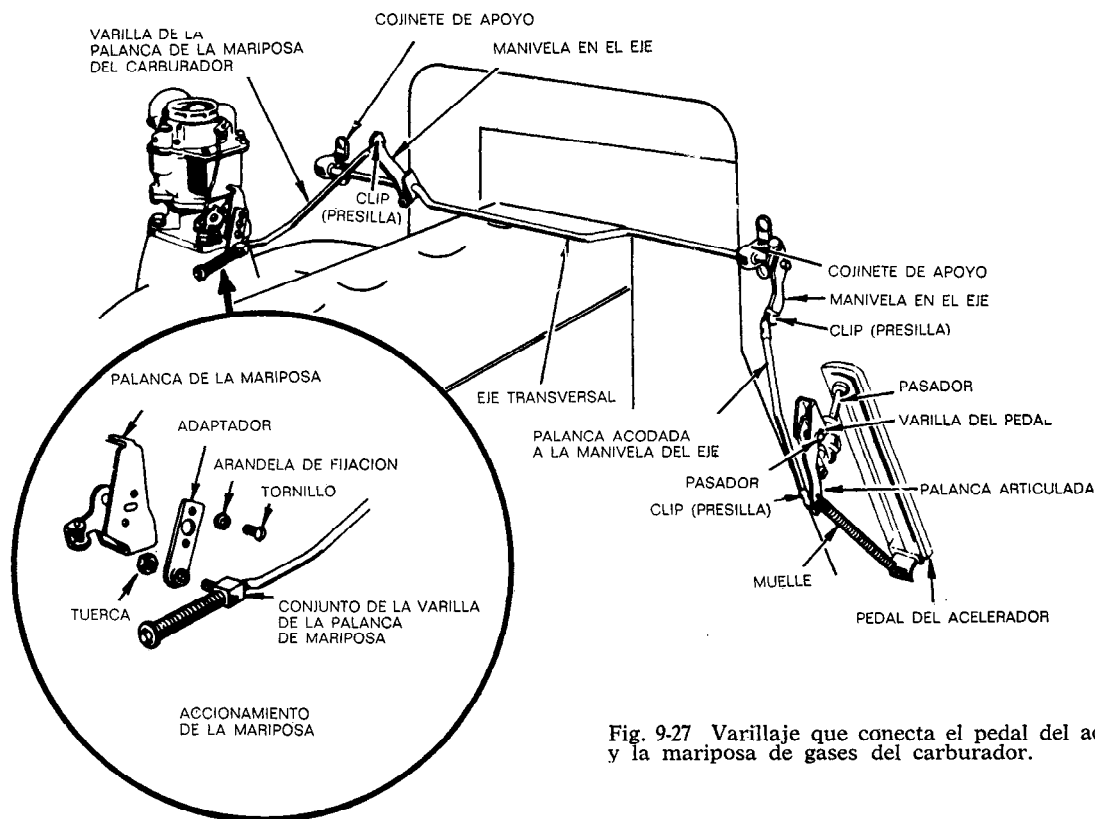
Varillaje que conecta el pedal del acelerador y la mariposa de gases del carburador.
